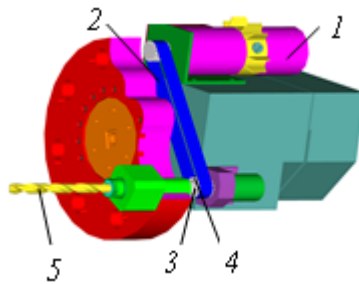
Схема шестипозиционной револьверной головки с вращающимся инструментом: 1 – приводной двигатель; 2 – зубчатая ременная передача; 3, 4 – полумуфты; 5 – инструмент
